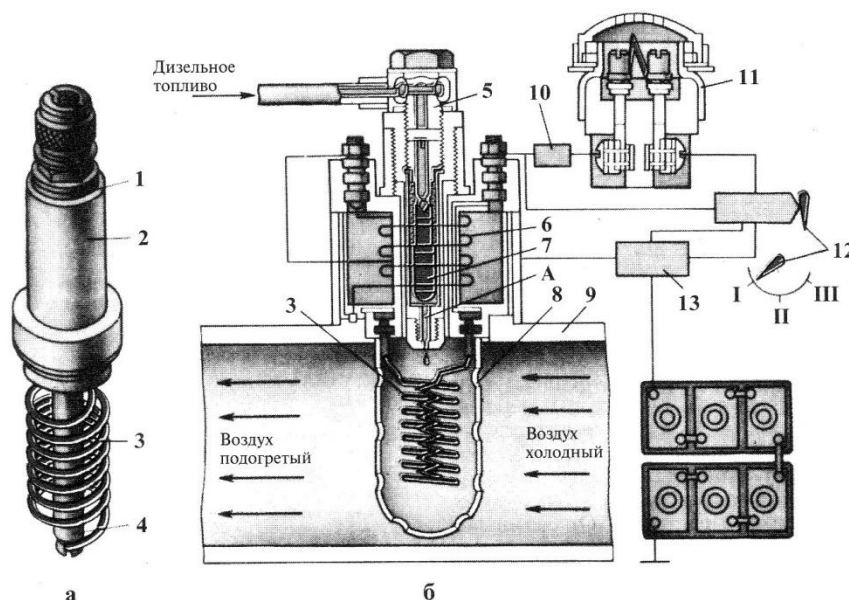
Приспособления для облегчения пуска дизеля: а – свеча накаливания; б – схема электрофакельного подогревателя; 1 – изолятор; 2 – корпус; 3 – спираль накаливания; 4 – стержень; 5 – полый болт; 6 – электромагнит; 7 – клапан; 8 – кожух; 9 – впускной трубопровод; 10 – резистор; 11 – контрольный элемент; 12 – ключ запуска двигателя; 13 – реле; А – топливоподводящий канал
